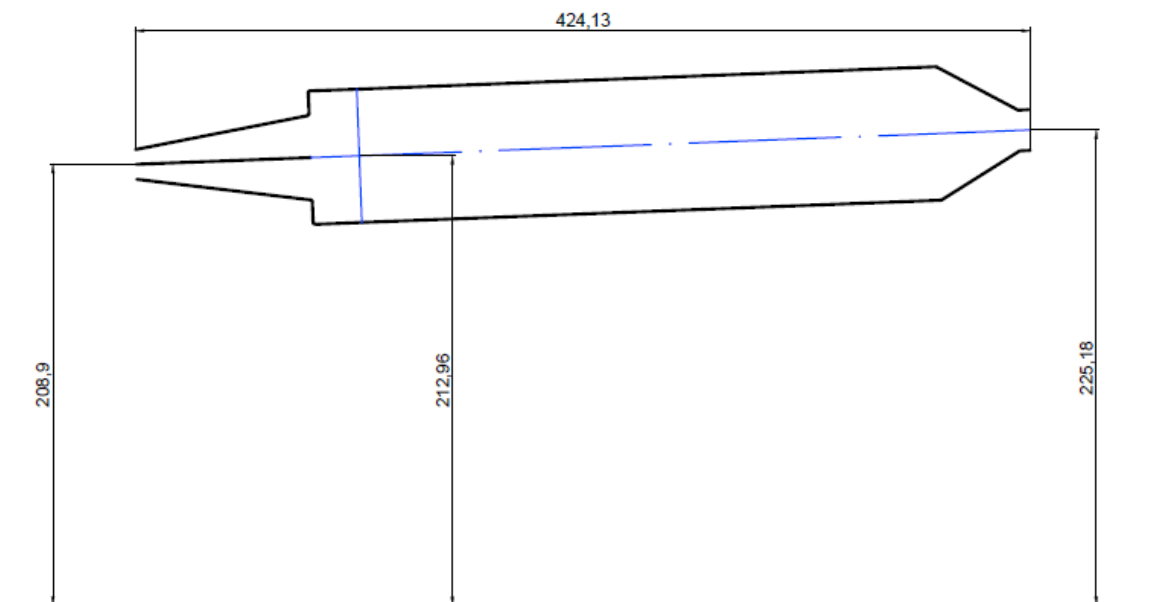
Esquema de la cámara de combustión con dimensiones axiales y radiales (en mm)
